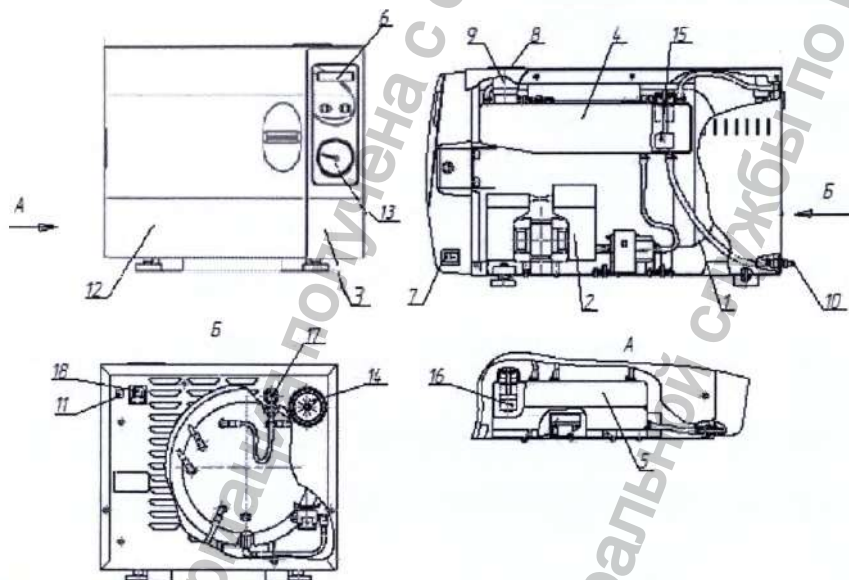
Внешний вид стерилизатора парового ГКа-25-ПЗ в вариантах исполнения КИУС.942711.004-08 и КИУС.942711.004-09 (вид спереди см. Рисунок 1а):
